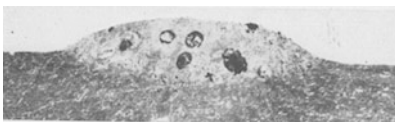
Fehlerhafte Nickelblechschweißung.
